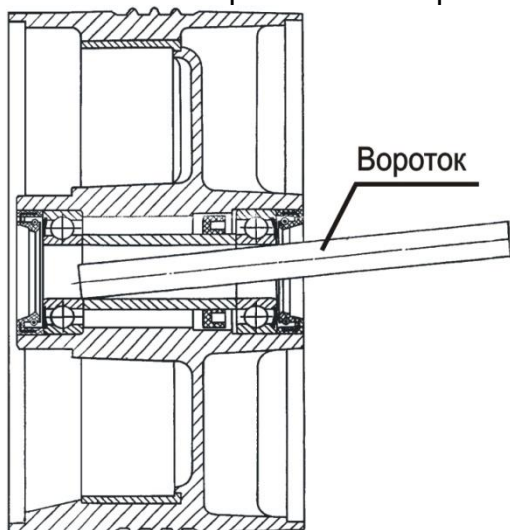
Выпрессовка подшипников и сальников из ступицы колеса
